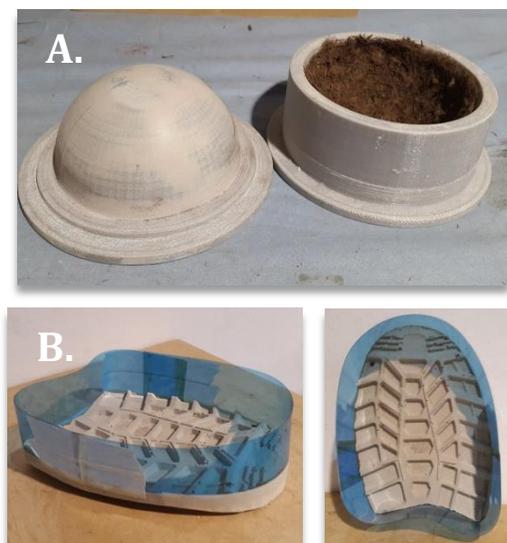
Métodos de moldeado. A. Molde semiesfera impreso en 3D.
